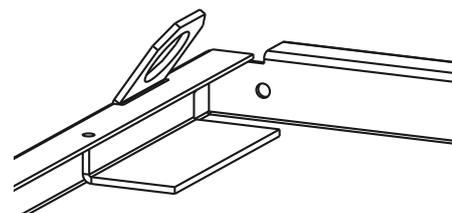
Gancio di sollevamento installato sul telaio del tetto
